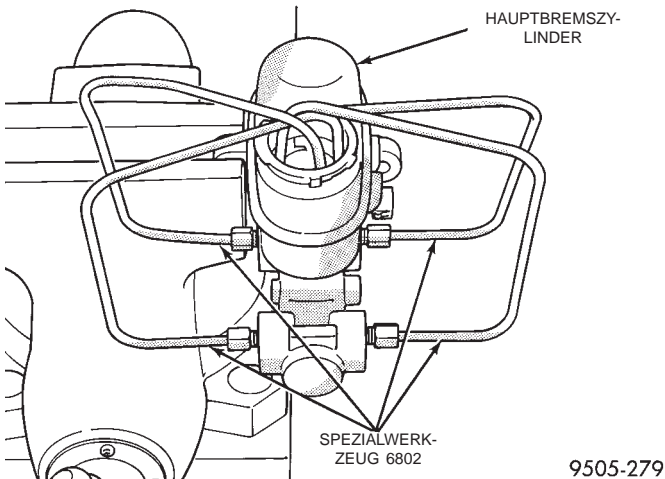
Entlüftungsschläuche am Hauptbremszylinder befestigt (Fahrzeuge mit ABS)
